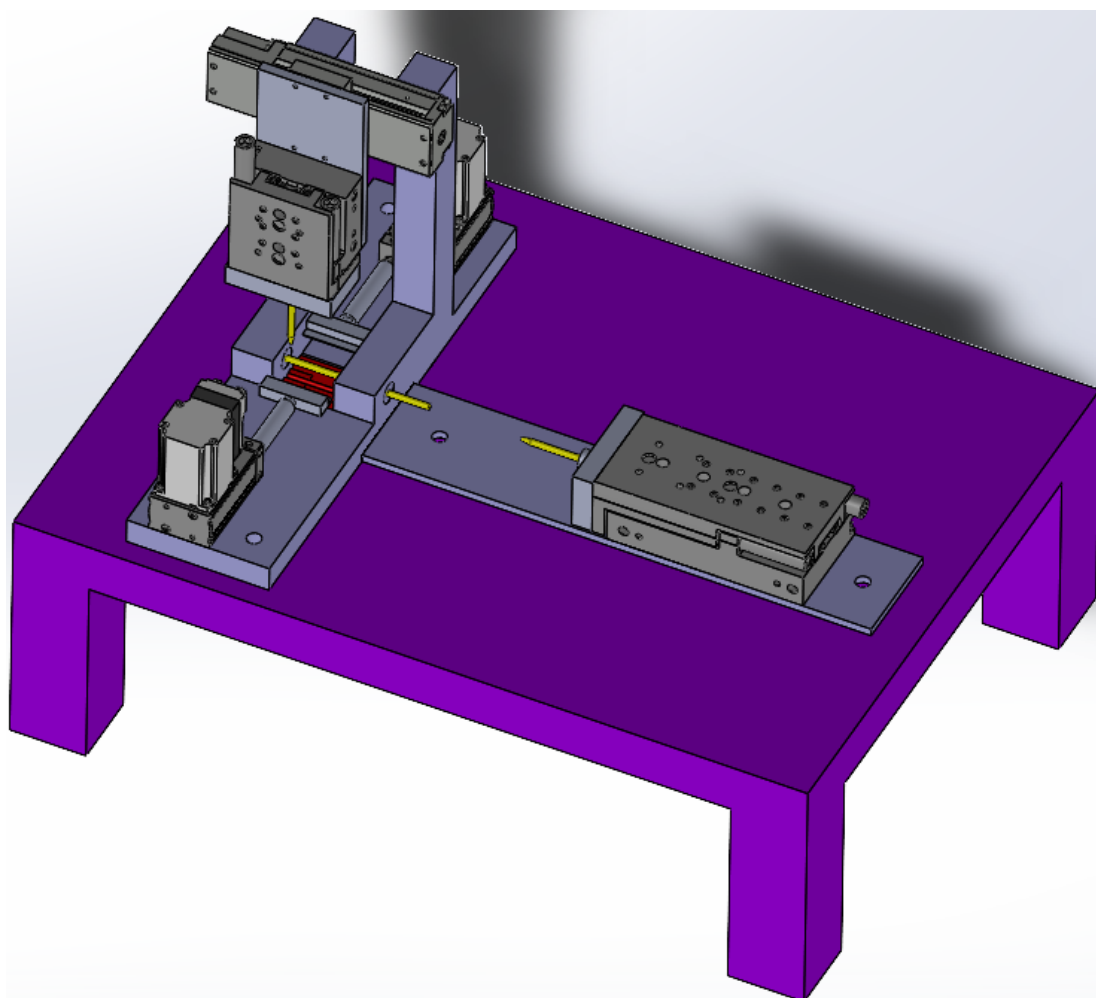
Система автоматической микроконтактной сварки
